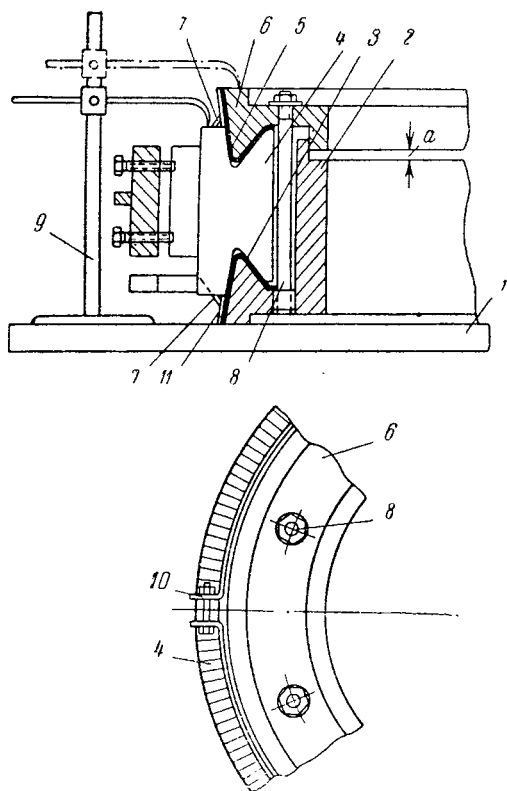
Схема сборки, опрессовки и выверки крупных коллекторов.
